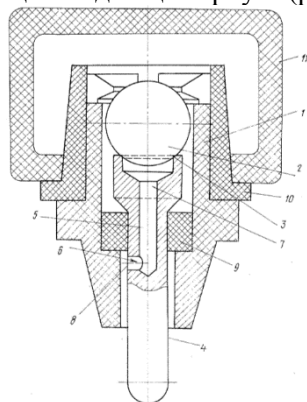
Конструктивная схема поилки для сельскохозяйственных птиц: 1 – водоподводящий сосуд; 2 – корпус; 3 – седло; 4 – сферический клапан; 5 – щели; 6 – поверхность клапана; 7 – рычаг; 8 – противовес; 9 – скоба
